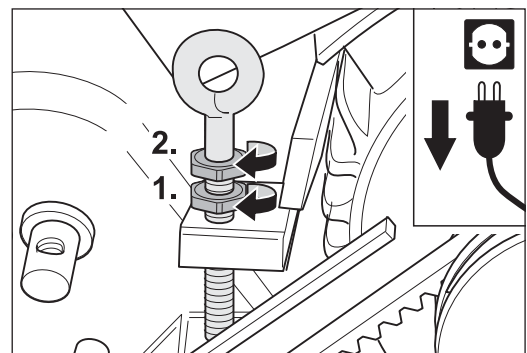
Zum Spannen des Antriebsriemens die Ringschraube am Motor im Uhrzeigersinn drehen (1.).
